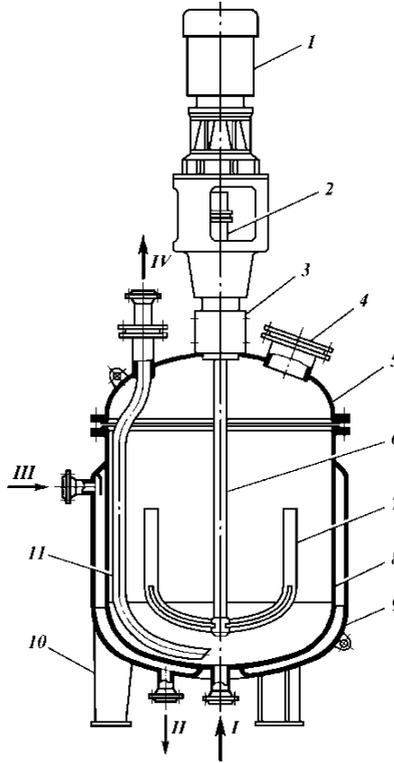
Реактор идеального смешения с рубашкой и перемешивающим устройством: 1 – электродвигатель; 2 – муфта; 3 – узел уплотнения вала; 4 – люк-лаз; 5- крышка; 6- вал; 7- якорная мешалка; 8- корпус; 9- рубашка; 10- опорные лапы; 11- труба для вывода продукта
